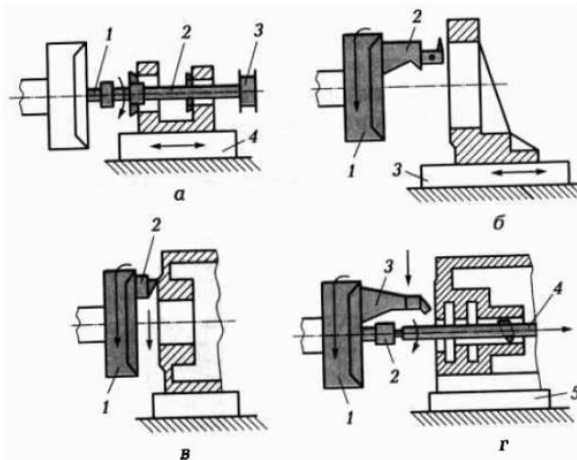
Способи обробки заготовок на горизонтально-розточувальному верстаті
